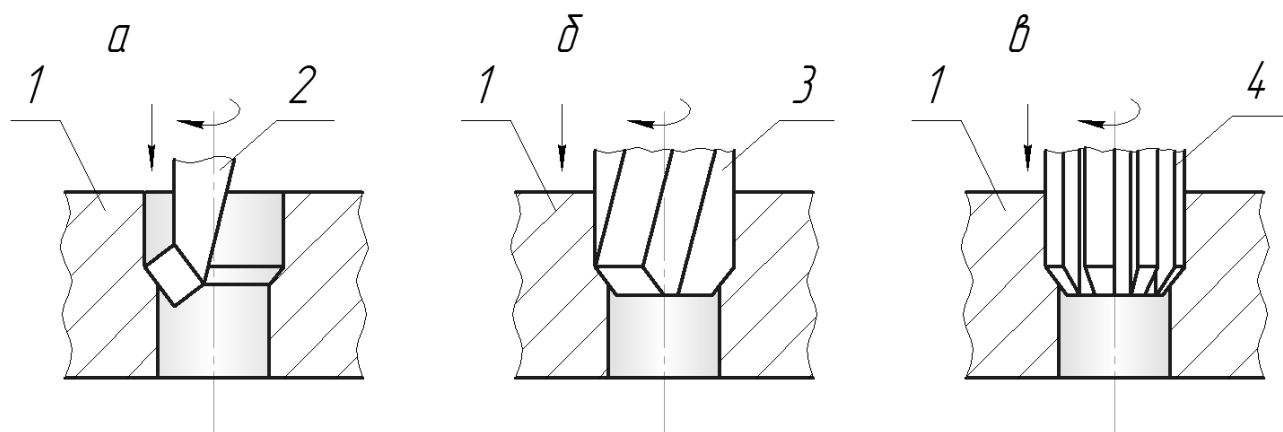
К задаче Б.11: Обработка отверстия: а – растачивание; б – зенкерование; в - развёртывание. 1 – заготовка; 2 – расточной резец; 3 – зенкер; 4 – развёртка.
